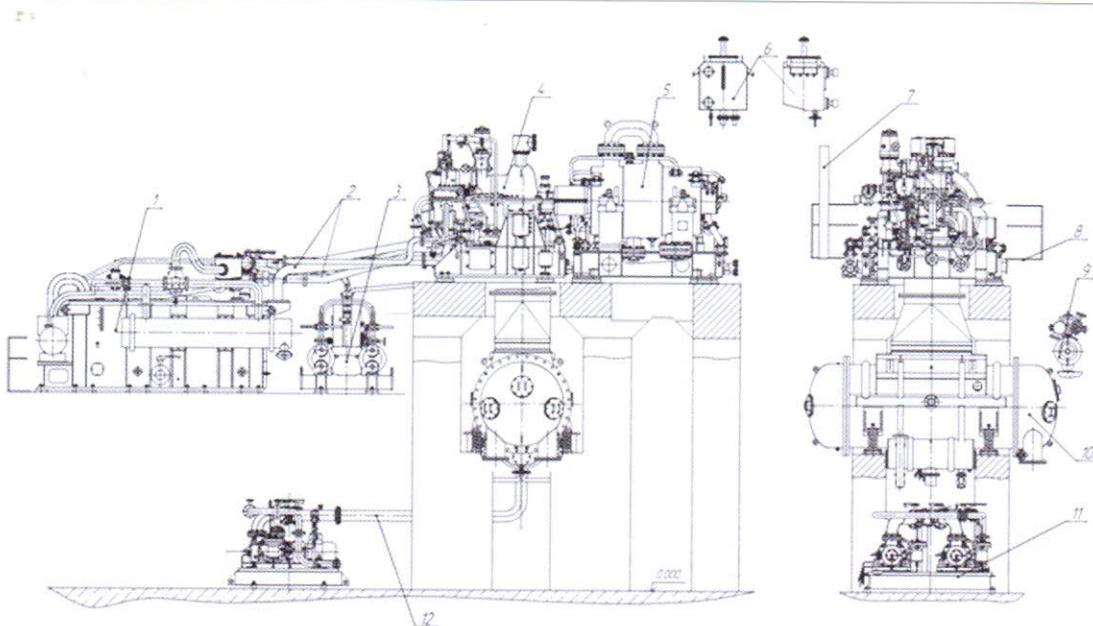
Установка компрессорная центробежная 4ГЦ2-55/10-40 У.1
